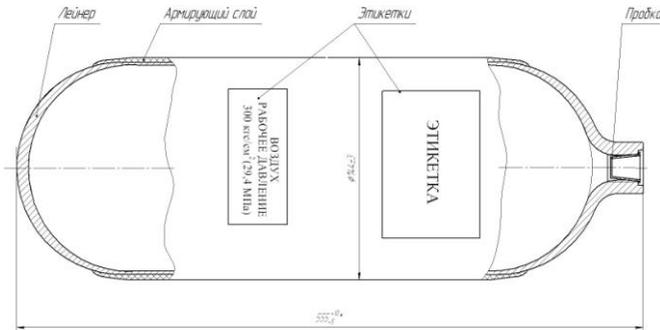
Баллон металлокомпозитный облепченный БК-7-300С
